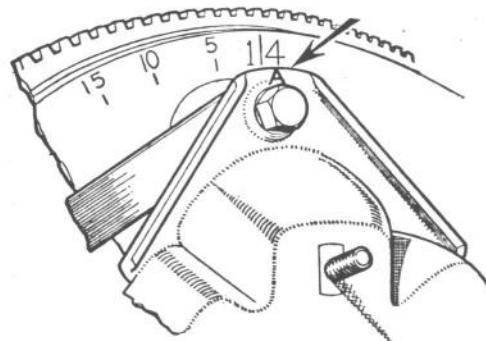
Referencias de montaje en el volante del motor y en la campana del mecanismo de embrague.
